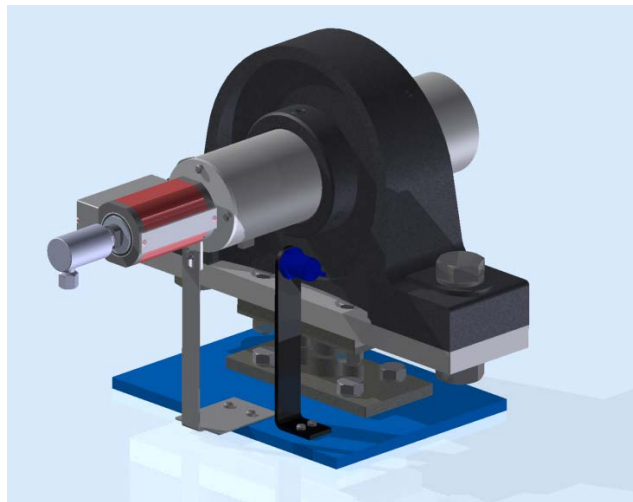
Vista general. S'observa el braç de parell amb el col·lector, juntament amb els altres components fixats a l'estructura fixa.
